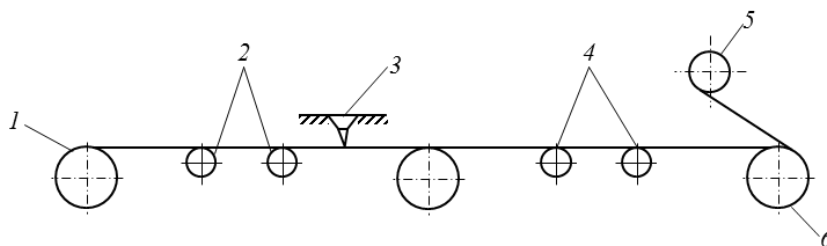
Схема изготовления пленочного связующего при помощи фильеры:
